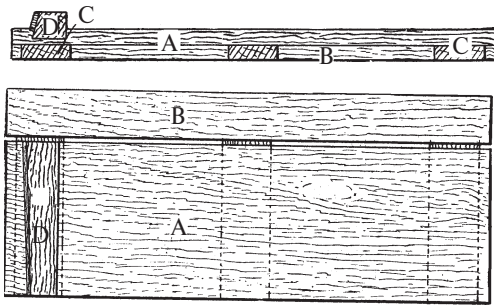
и 44. — Боковой вид и общий план верстачной доски
